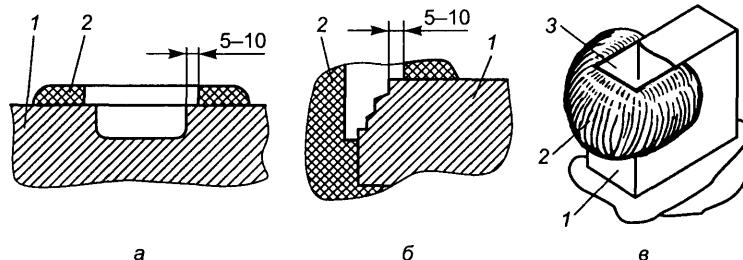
Схема изготовления форм при дуговой сварке с предварительным нагревом:
